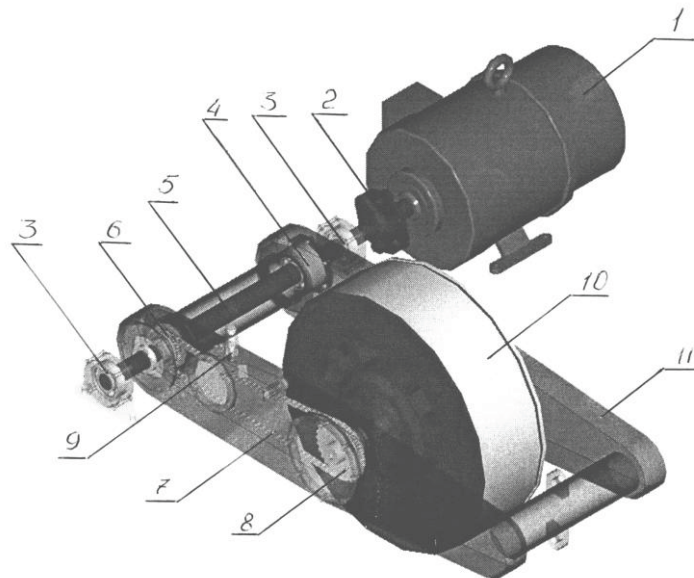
Схема силового приводу стенду, де: 1 - електродвигун постійного струму; 2 - сполучна обгонна муфта; 3, 4 - опорні підшипники; 5 - провідний вал; 6 - провідна зірочка; 7 - ланцюгова передача; 8 - ведена зірочка; 9 - натягач ланцюга; 10 - біговий барабан-маховик; 11 - рама кріплення бігового барабана-маховика
